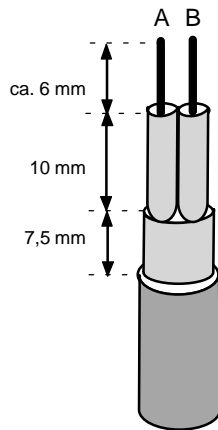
Konfektionierung der Leitungsenden für die Montage des Busanschlußsteckers mit axialem Kabelabgang
